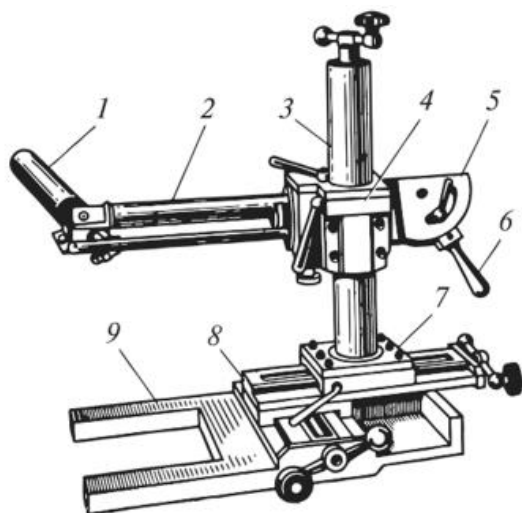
Манипулятор для токарного станка с перемещением плазматрона вручную в зоне обработки:
